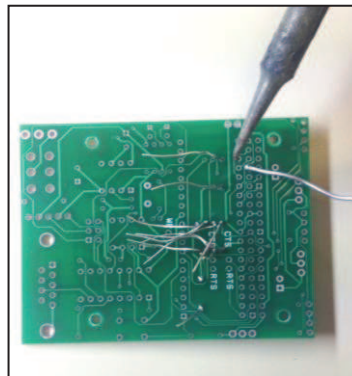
Soldadura de la placa (Font pròpia).
